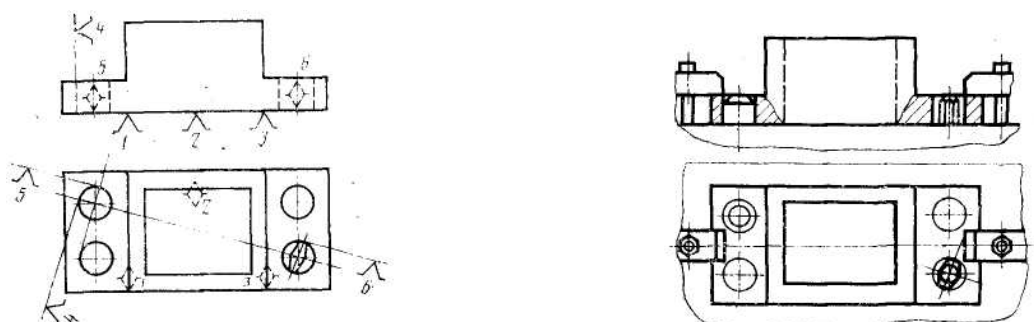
Схема базирования заготовки по плоскости и двум отверстиям в лапах
